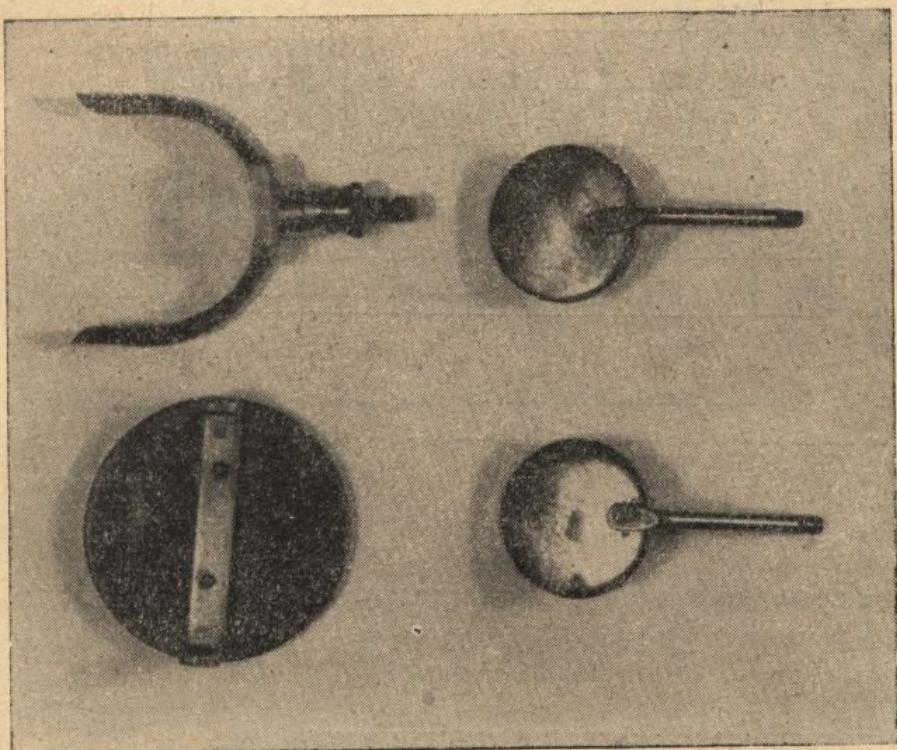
Детали, переведенные с пайки на сварку.
